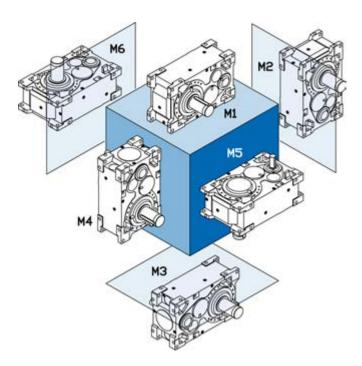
Монтажные положения цилиндрических соосных редукторов со стандартными монтажными поверхностями
